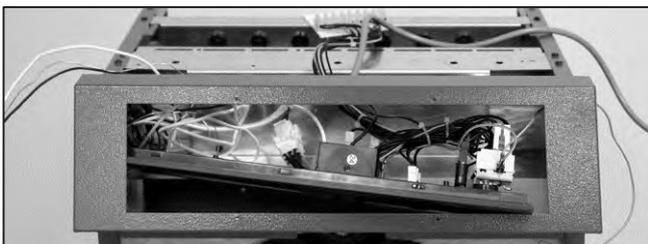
THETA-Kesselgrundschaltfeld von hinten-oben durch den Schaltfeldausschnitt stecken.
